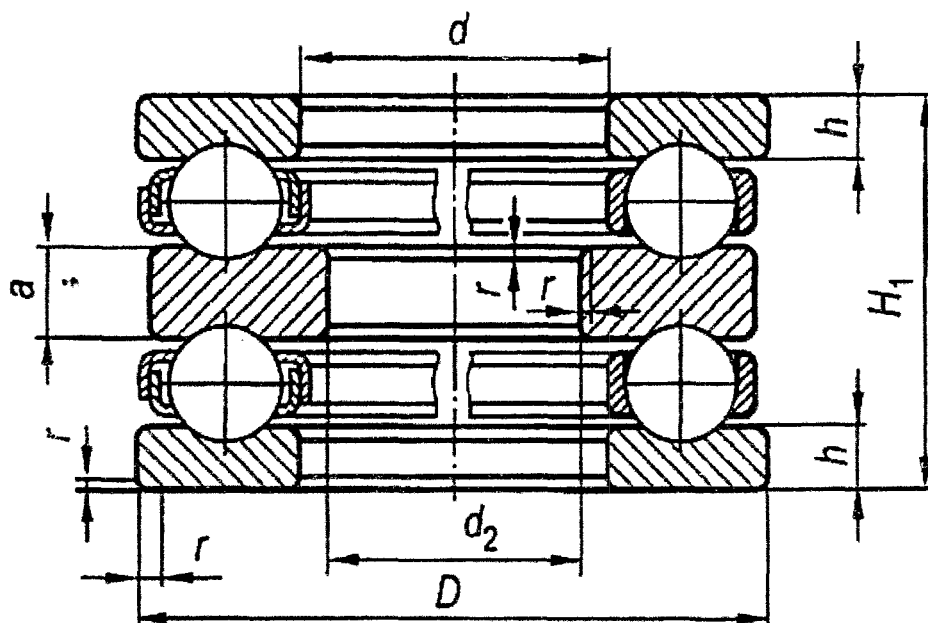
Подшипник шариковый упорный двойной исполнения 38 000 H
